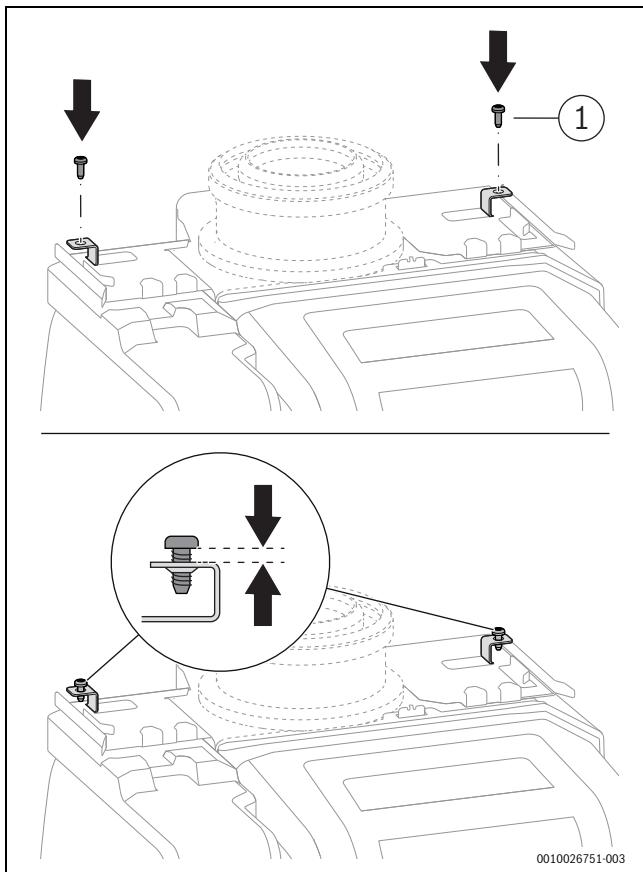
Schrauben für die Oberseite der Geräteverkleidung locker ein-drehen
